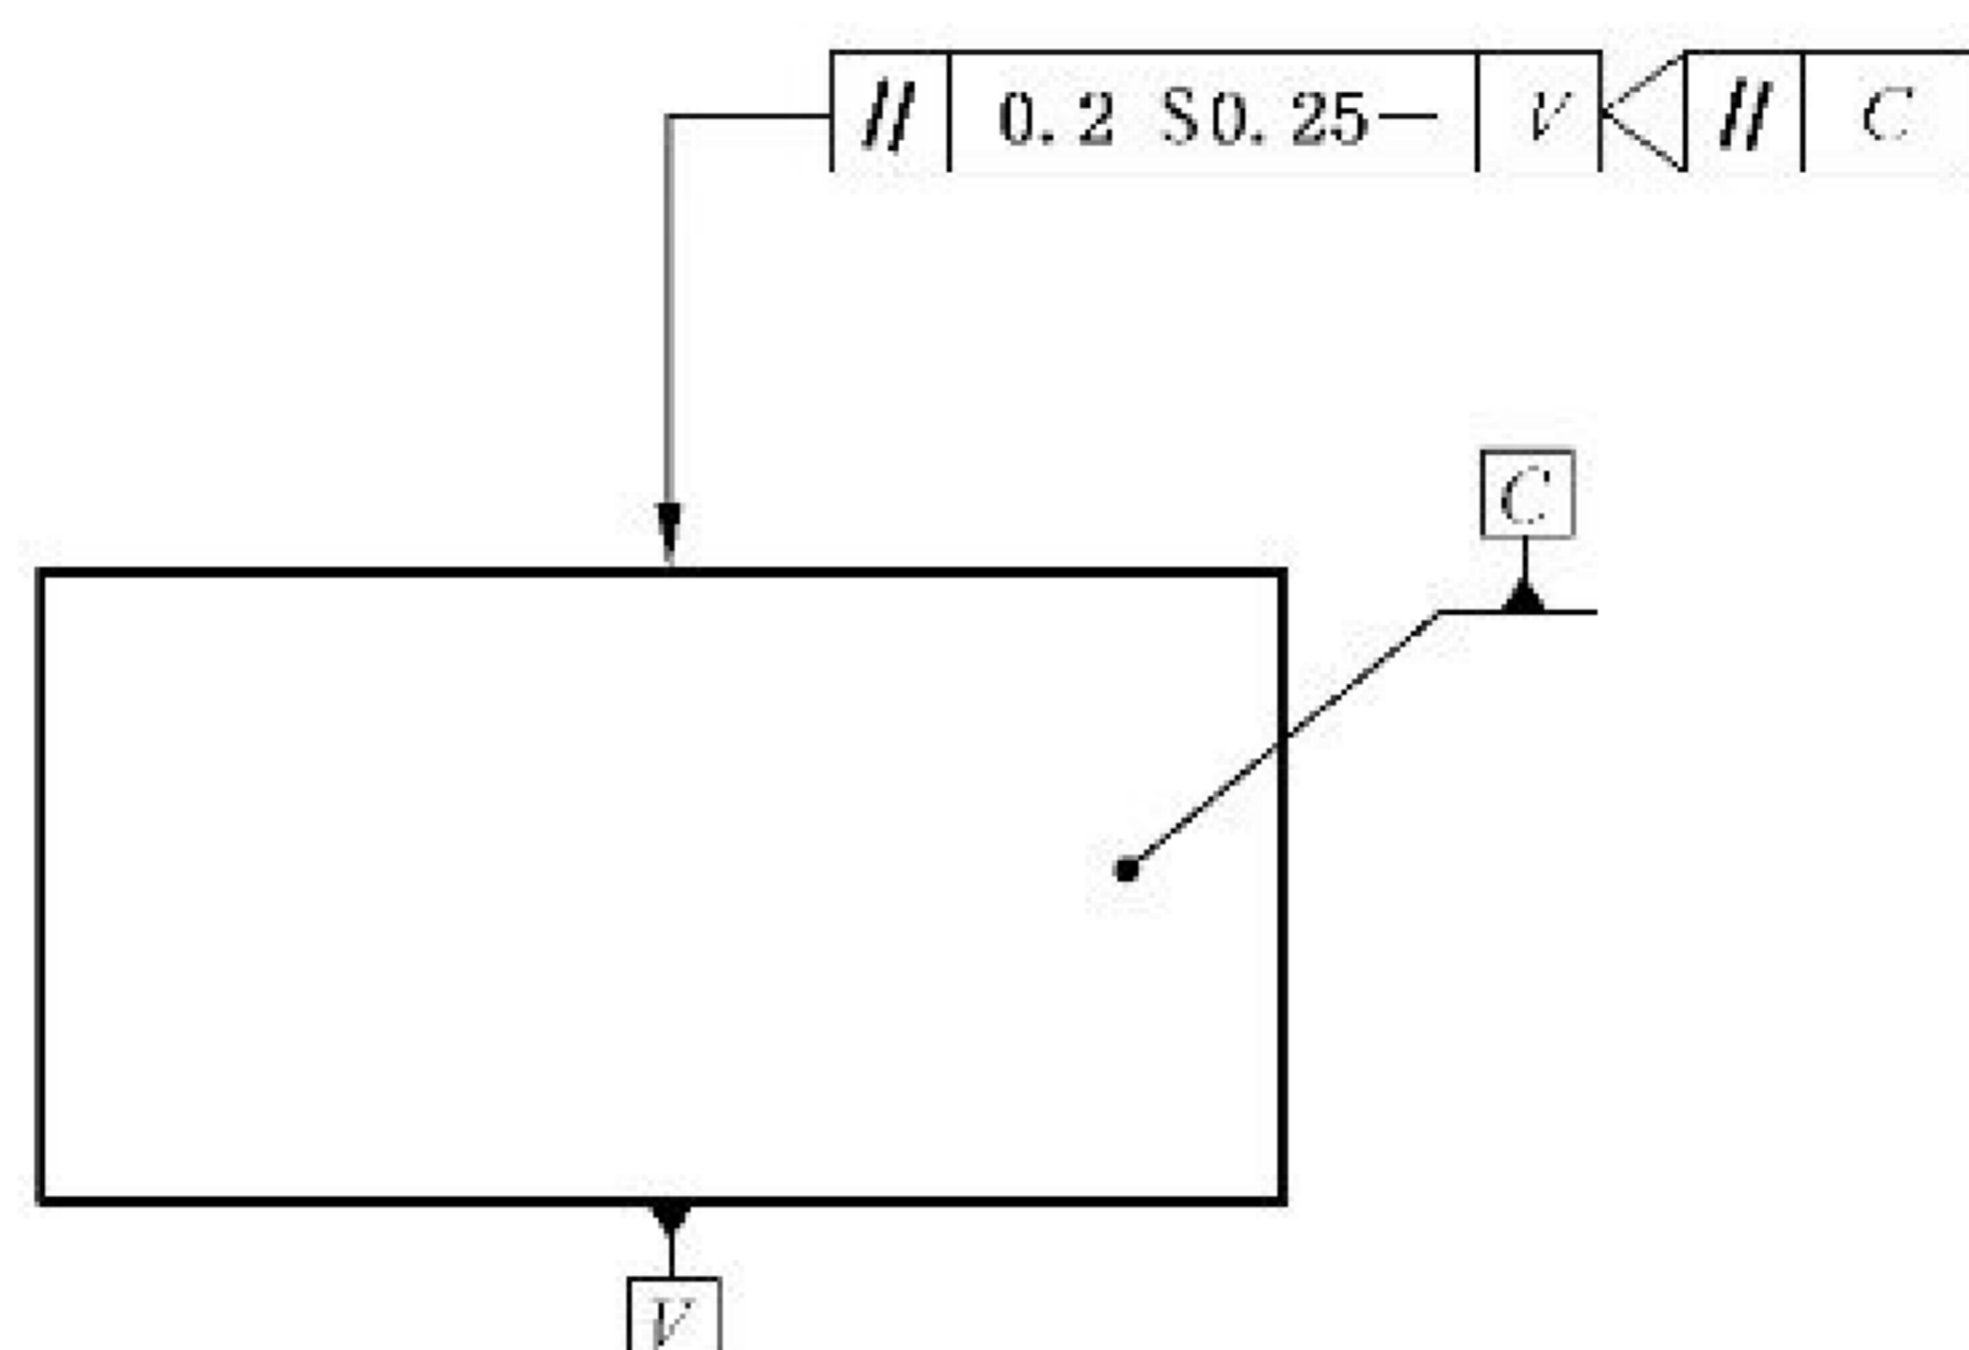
使用长波通滤波器的平行度公差示例
